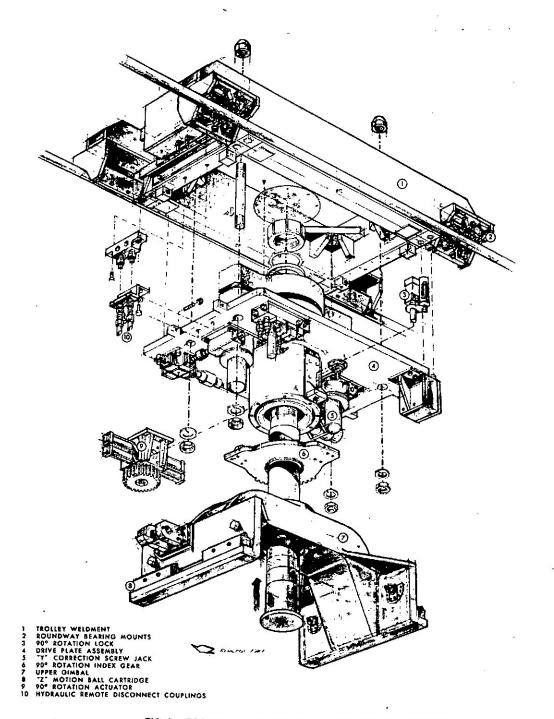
TROLEY DEL CARRO DE LA MAQUINA DE RECAMBIO
